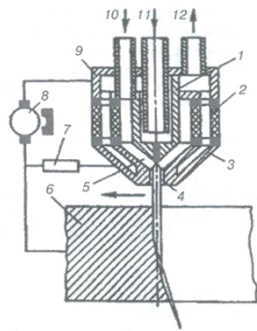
Плазматрон для резки: 1 - электрод (катод); 2 - изолятор; 3 - формирующий наконечник; 4 - столб дуги; 5 - дуговая камера; 6 - разрезаемый металл; 7 - устройство зажигания дуги; 8 - источник тока; 9 - корпус; 10 - подача рабочего газа; 11 - подача охлаждающей воды; 12 - слив воды
